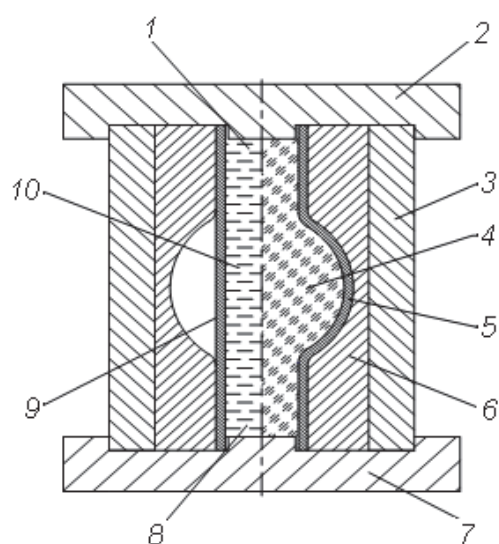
Штамп для раздачи трубчатой заготовки с использованием энергии расширения воды при её заморозке
